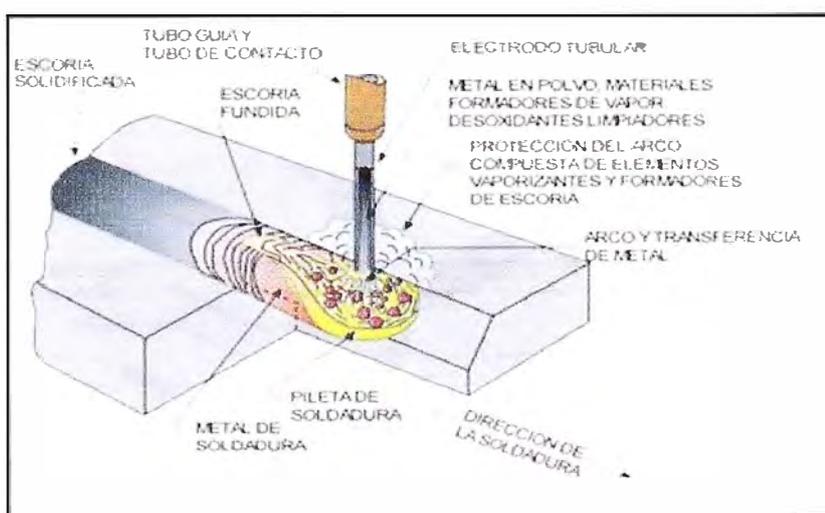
Proceso de Soldadura FCAW -S
